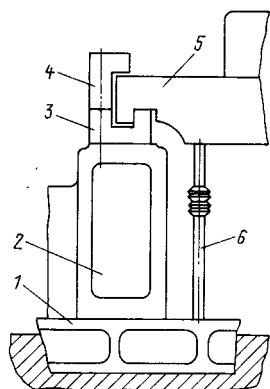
Установка дополнительной опоры под лапу для уменьшения силы, действующей со стороны лапы на корпус подшипника:
